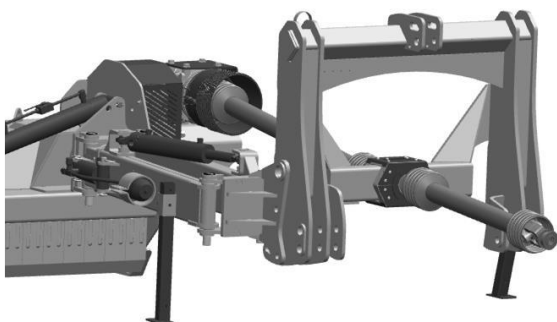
Общий вид комплекта сдвоенного карданного вала
